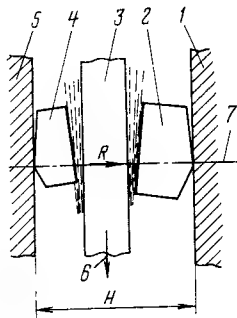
Положение гребня в упорном подшипнике (вид на упорный диск сверху): 1, 5 — корпус вкладыша; 2 — рабочий сегмент; 3 — гребень; 4 — установочный сегмент; 6 — направление вектора окружной скорости точки гребня, контактирующей с сегментом; 7 — ось турбины
